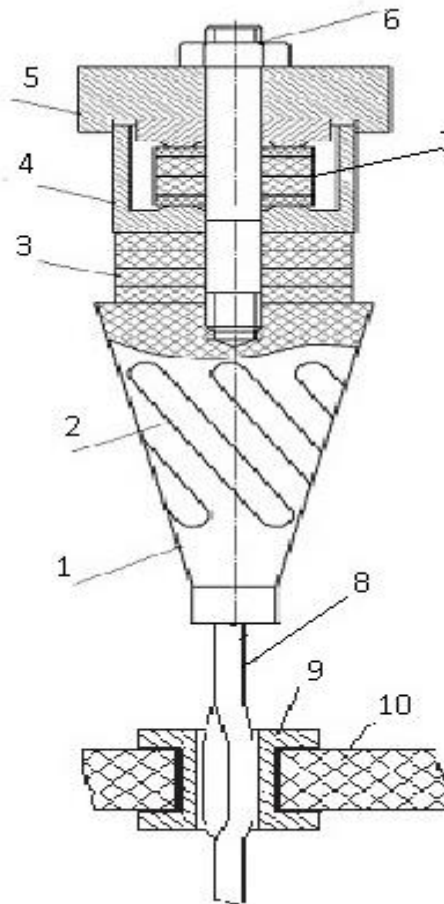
ультразвуковое устройство для запрессовки штырьков в платы
